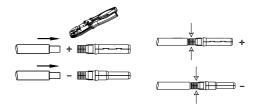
Inserimento dei cavi nelle viti di bloccaggio
